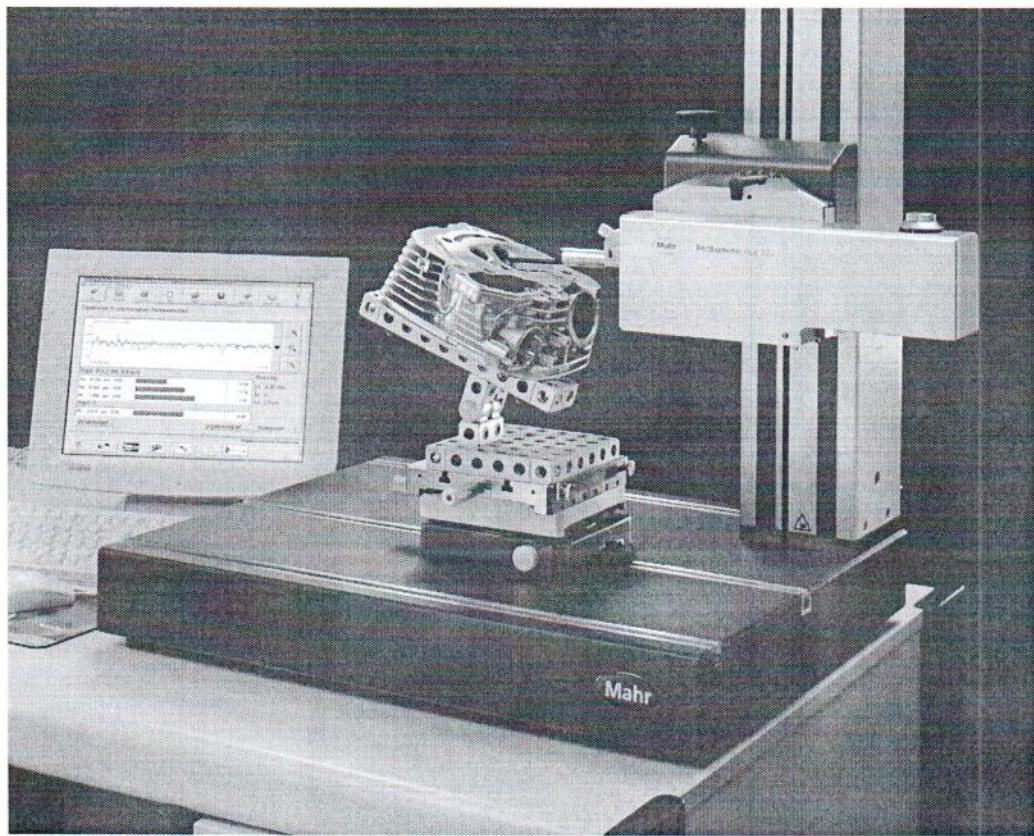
Внешний вид приборов для измерения шероховатости поверхности MarSurf XR20 в составе с GD 120
